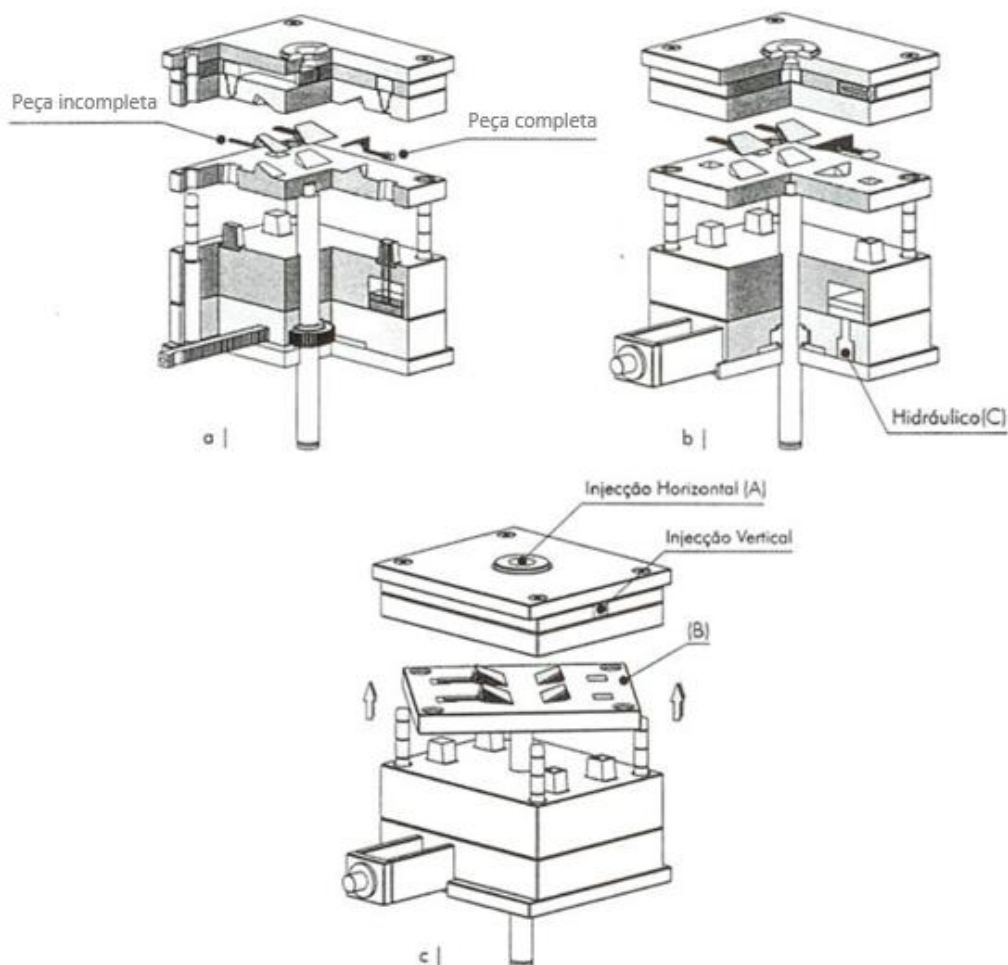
Molde bi-material: a) abertura do molde, b) abertura do molde e corte e c) abertura do molde com rotação da placa (CENTIMFE, 2003)
